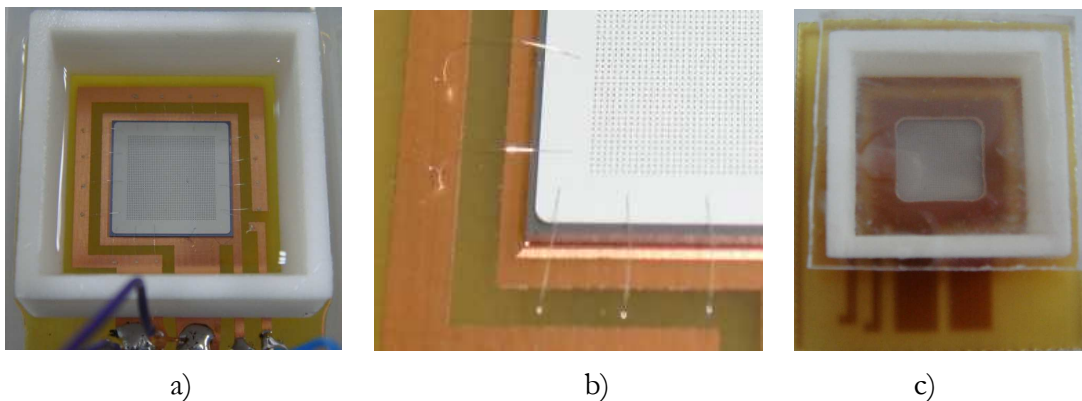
Photographies du package des diodes avec DRIM Cooler a) face avant, b) zoom sur la face avant, c) face arrière.
